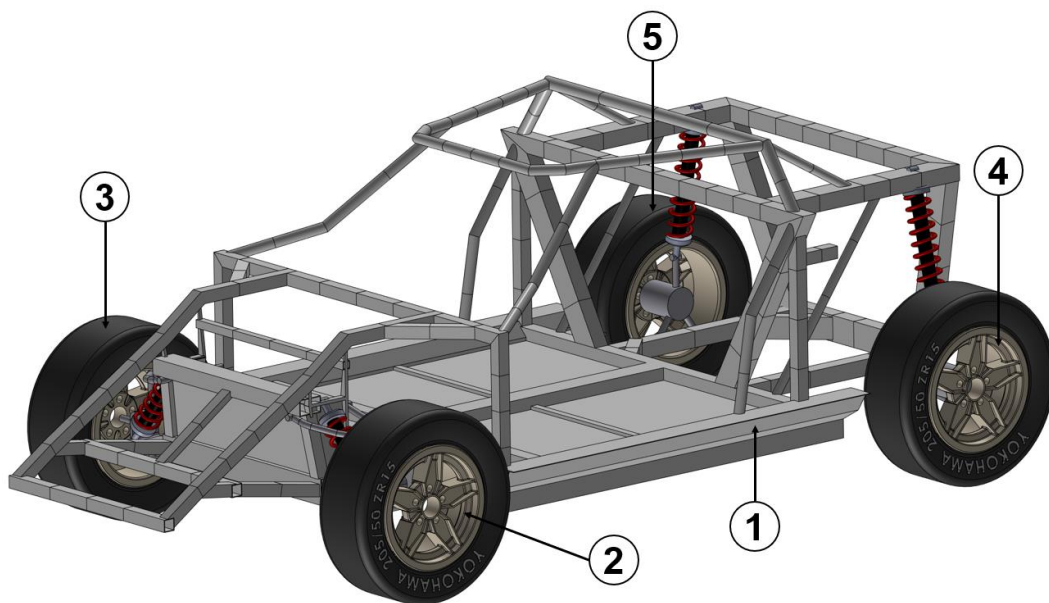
Estrutura do Chassis e Conjuntos Pneu-Jante.
